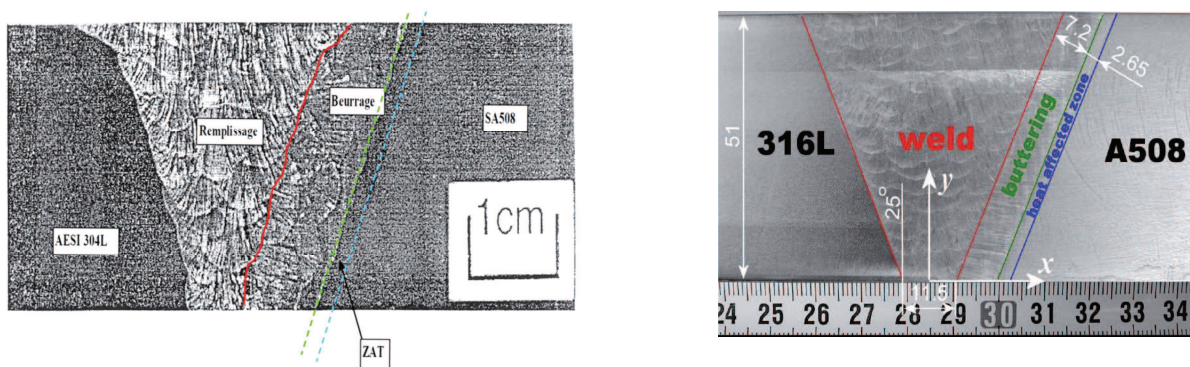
Soudures des maquettes BIMET (gauche) et ADIMEW (droite) [GIL 09]
